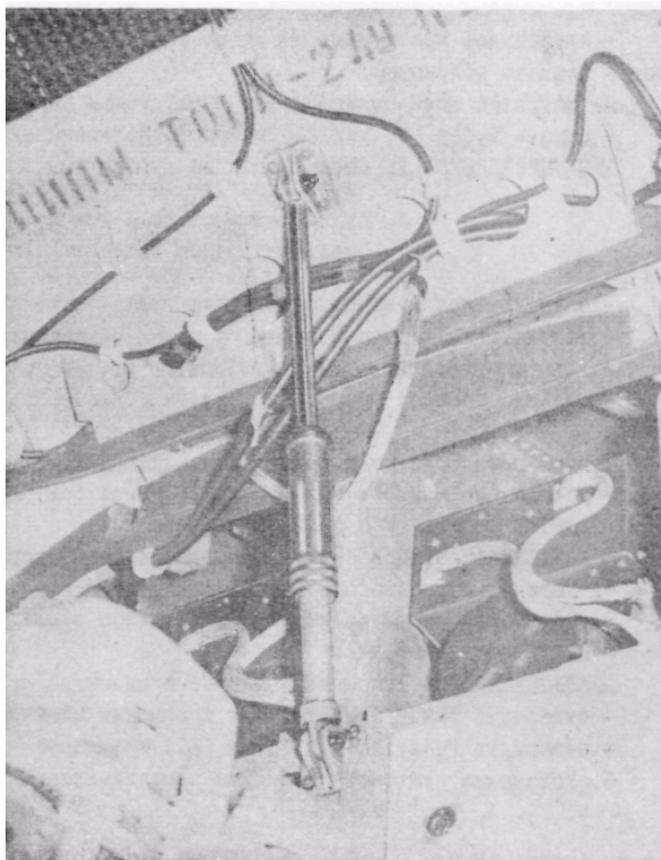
УСТАНОВКА УПОРНОГО ЦИЛИНДРА
